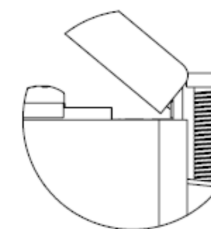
Detailní vyznačení místa pro zachycnutí krytky
